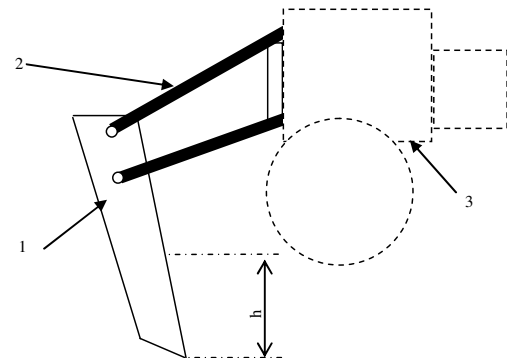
Конструктивна схема глибокорозпушувача ґрунту для присадибних ділянок: 1- робочий орган; 2- зчіпний механізм; 3- мотоблок; h - глибина обробітку
